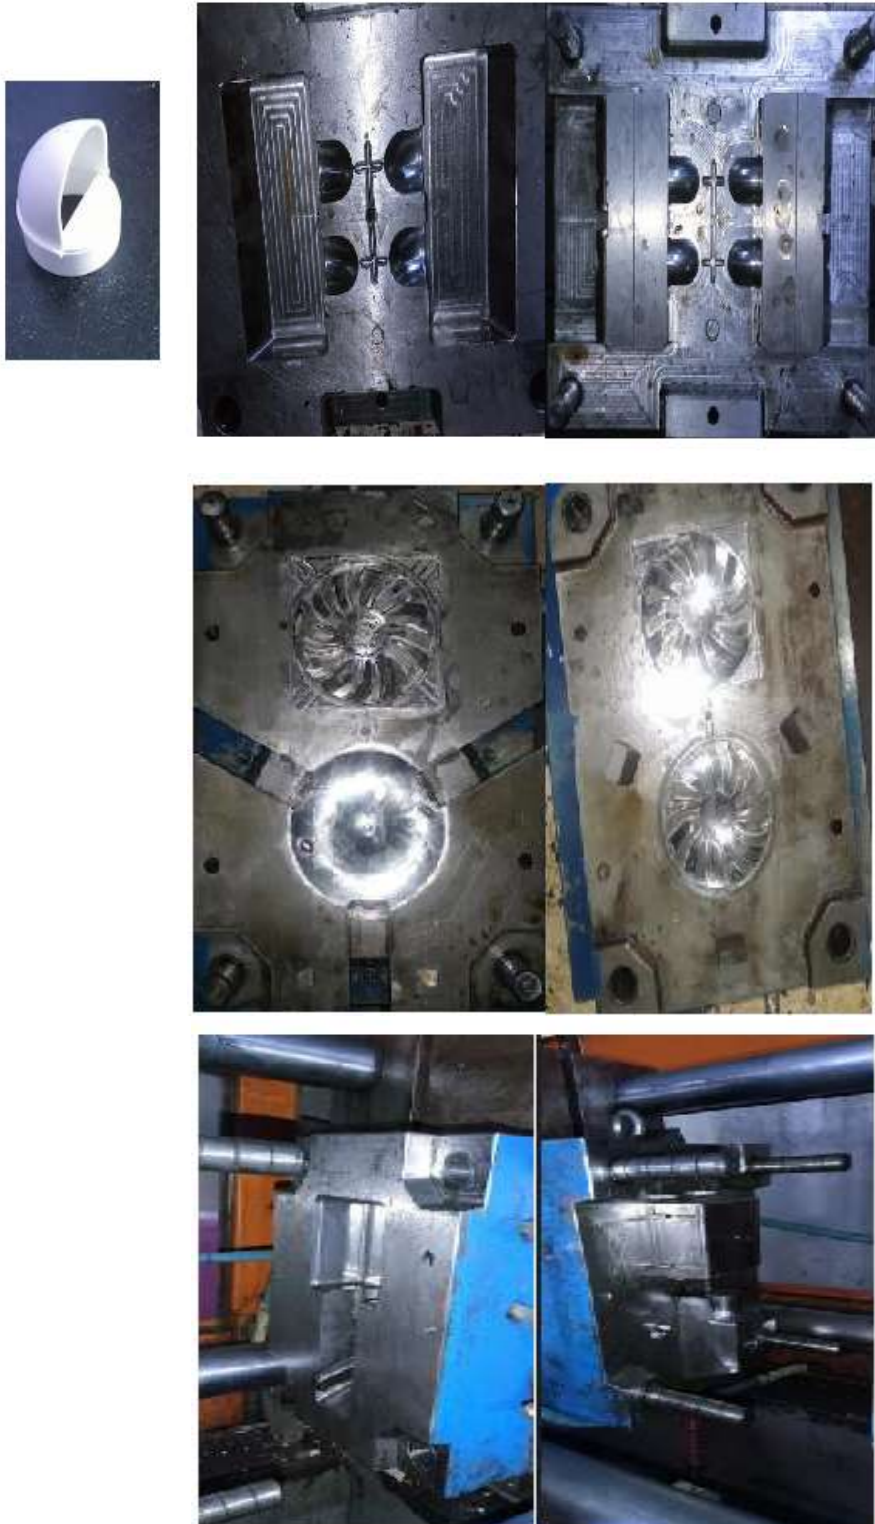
les déferant type de moule nécessaire pour fabrique le siphon
